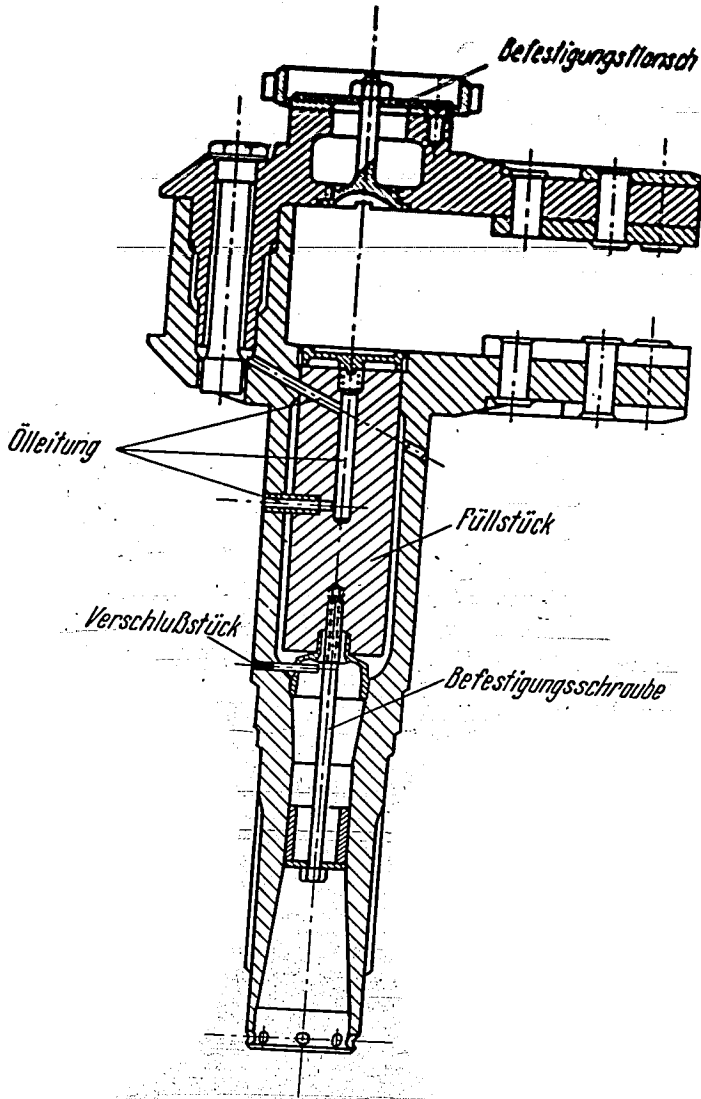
Schnitt durch die abgeänderte Kurbelwelle des BMW 132 - Einzylinder - Motor.
